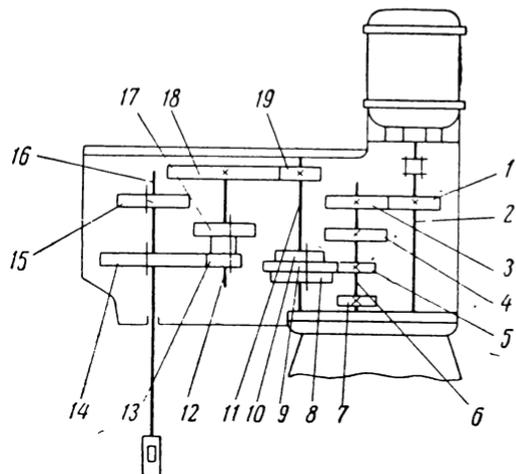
Схема коробки скоростей вертикально-сверлильного станка
